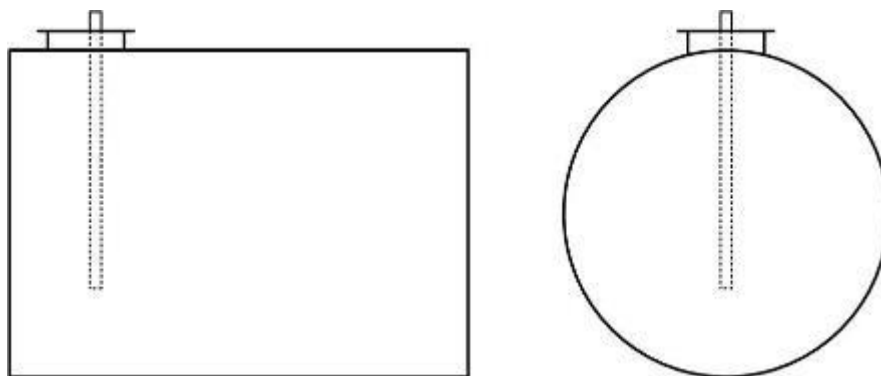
Эскиз общего вида резервуара РГС-10 № 5
